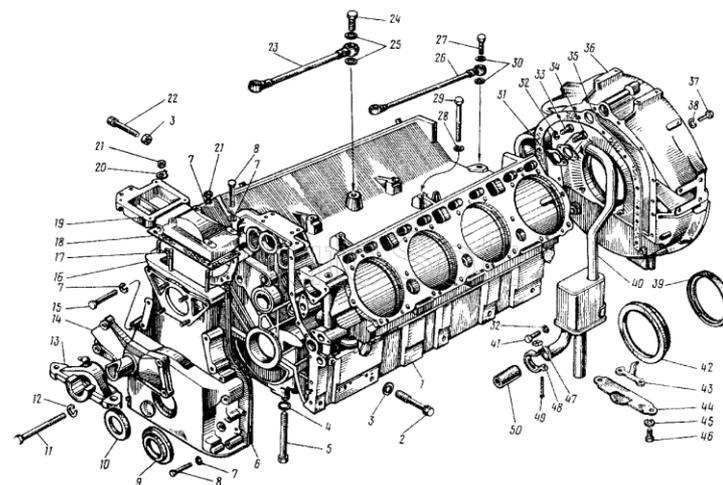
Блок цилиндров двигателя ЯМЗ-238НД
